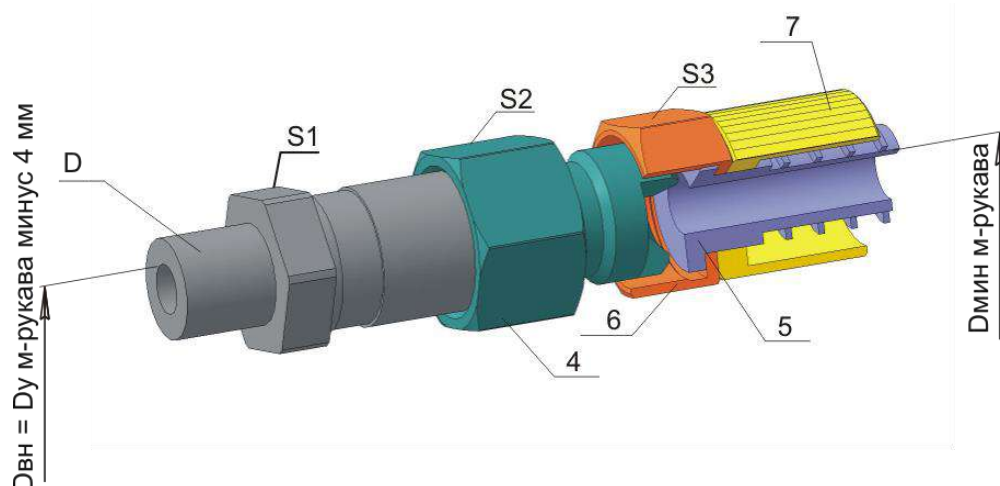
Конструкция кабельного ввода для монтажа кабеля в металлорукаве с ПВХ оболочкой
